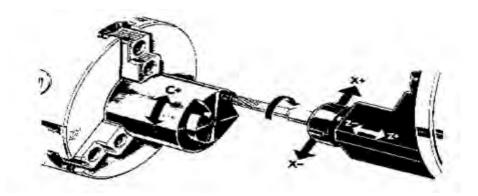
Пример получения криволинейной поверхности на торце заготовки за счёт одновременного перемещения вращающейся концевой фрезы (по X, Z) и поворота заготовки (по C)
